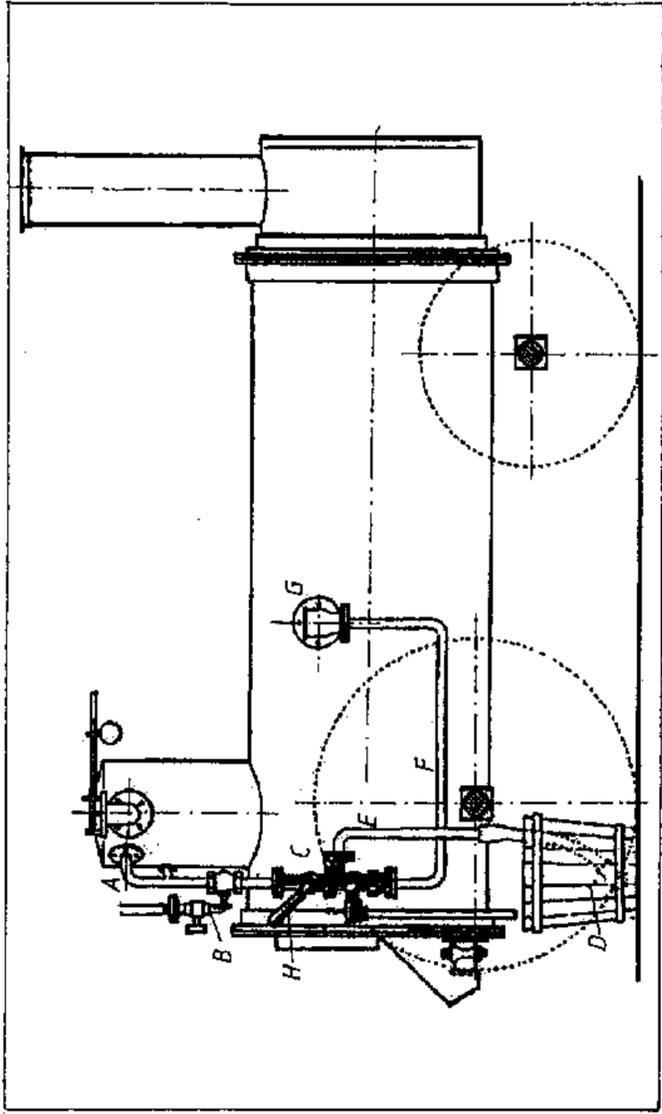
/2: Anlagenplan einer Speiseeinrichtung an einer verfahrenbaren Lokomotive
